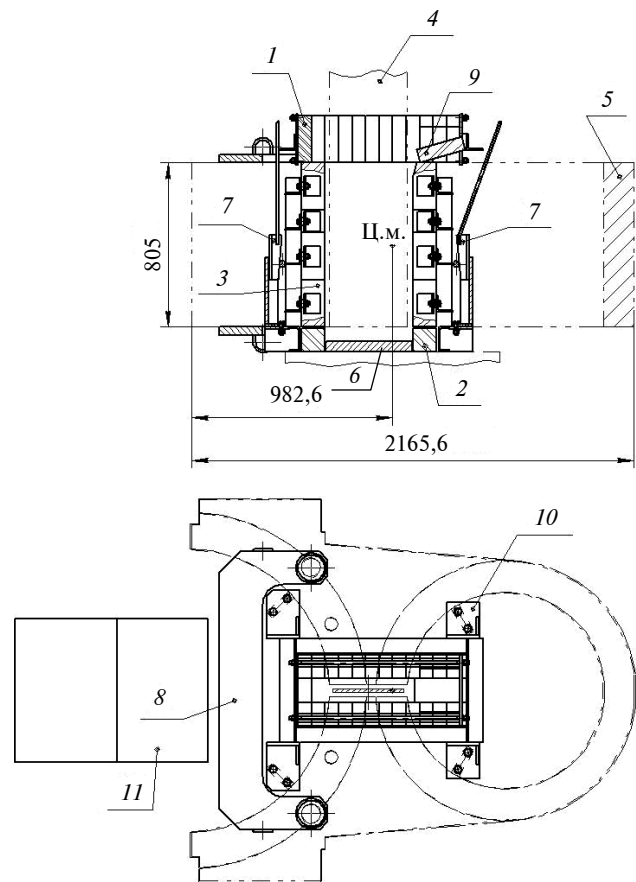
Схема складання шатуна під електрошлакове зварювання: 1 – верхня вивідна кишеня; 2 – нижня вхідна кишеня; 3 – бокові футеровані стінки; 4 – витратний електрод; 5 – зварювана деталь (шатуна); 6 – затравки; 7 – притисний пристрій; 8 – скоби фіксуючі; 9 – заливна воронка; 10 – уловлювачі; 11 – установка У560
